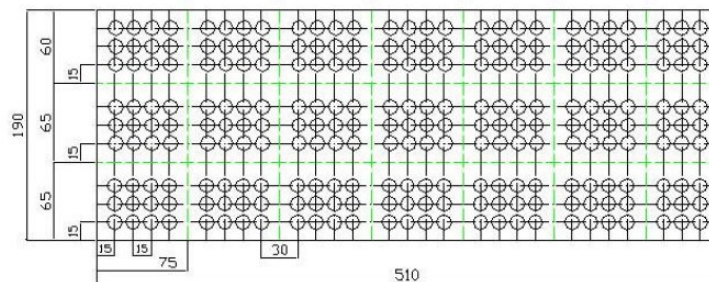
Desenho esquemático do corpo de prova de ferro fundido cinzento
